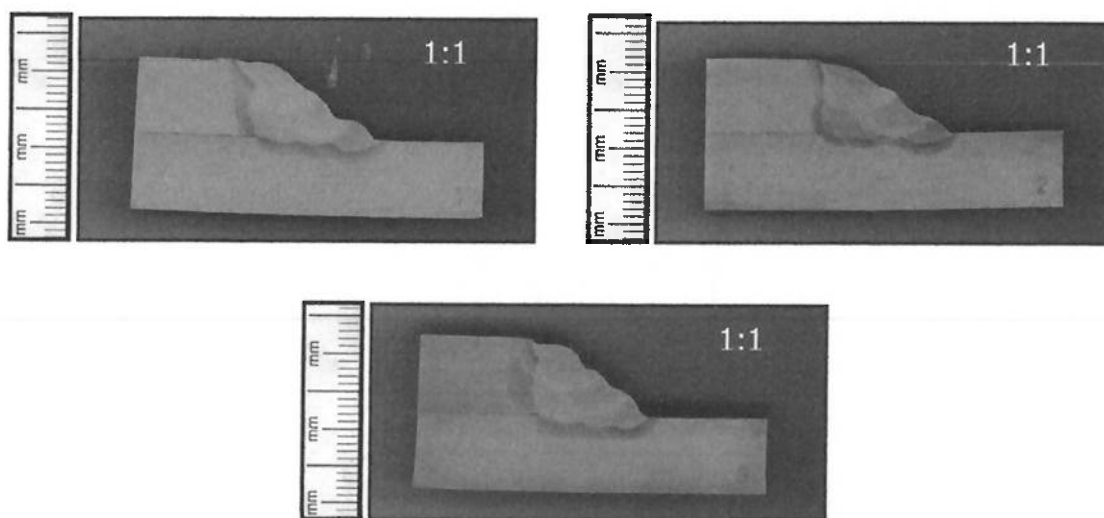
Ensaios de macrografia da junta soldada com maior energia de soldagem (1,58 kJ/mm).
